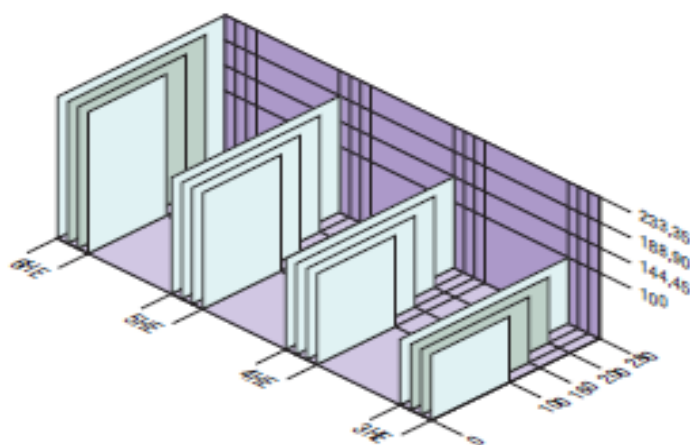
Типоразмеры печатных плат Евромеханика
